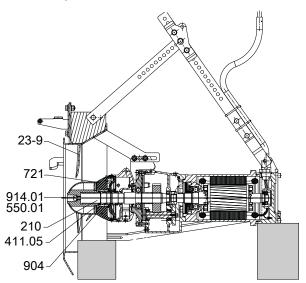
Desmontaje de la hélice axial; Amaline 500, 600
